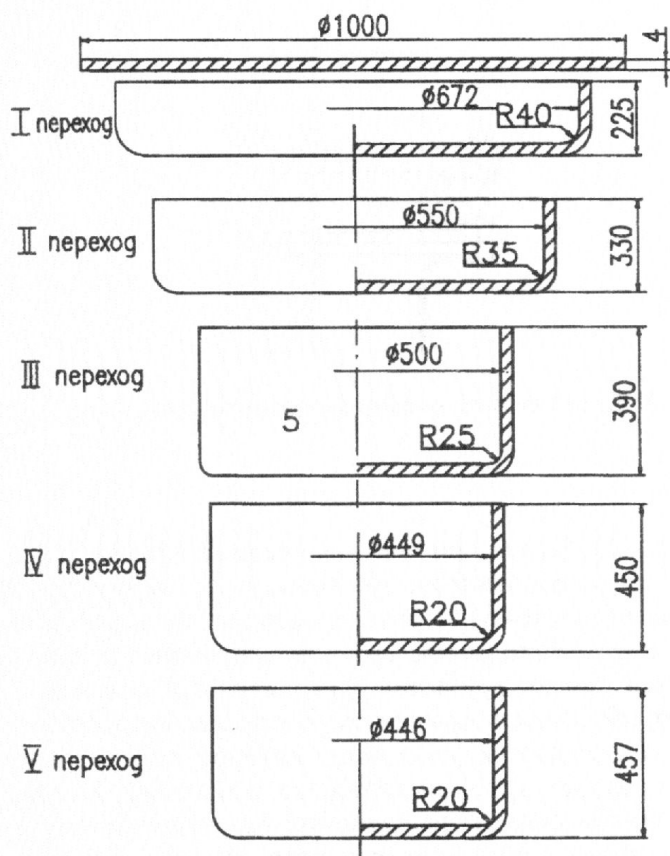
Последовательность операций вытяжки заготовки сильфона
